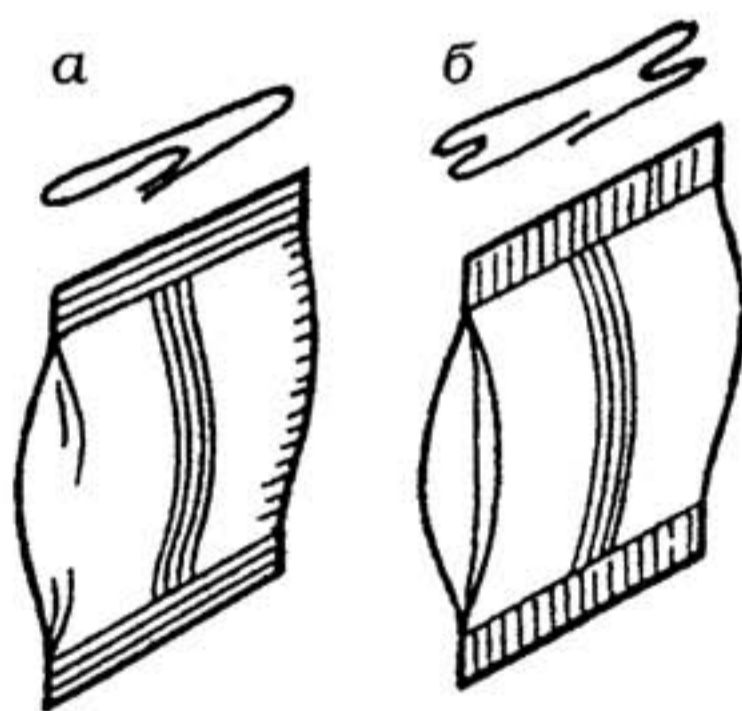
Пакеты с одним продольным и двумя поперечными швами: а — плоский; б — с боковыми складками
